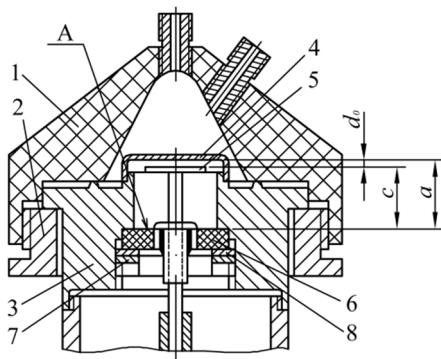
Ємнісний перетворювач тиску: 1 – кришка; 2 – гайка; 3 – корпус; 4 – мембрана; 5 – електрод; 6 – ізоляційна шайба; 7 – кільце; 8 – шайба
